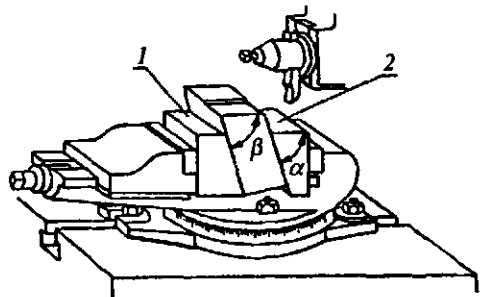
Схема установки и закрепления в тисках бруска под углом
